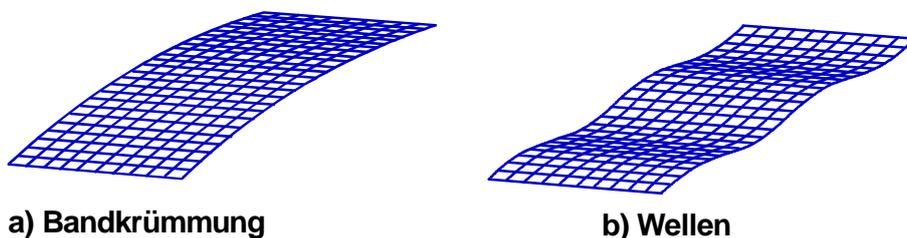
abwickelbare Planheitsfehler [buch73]
